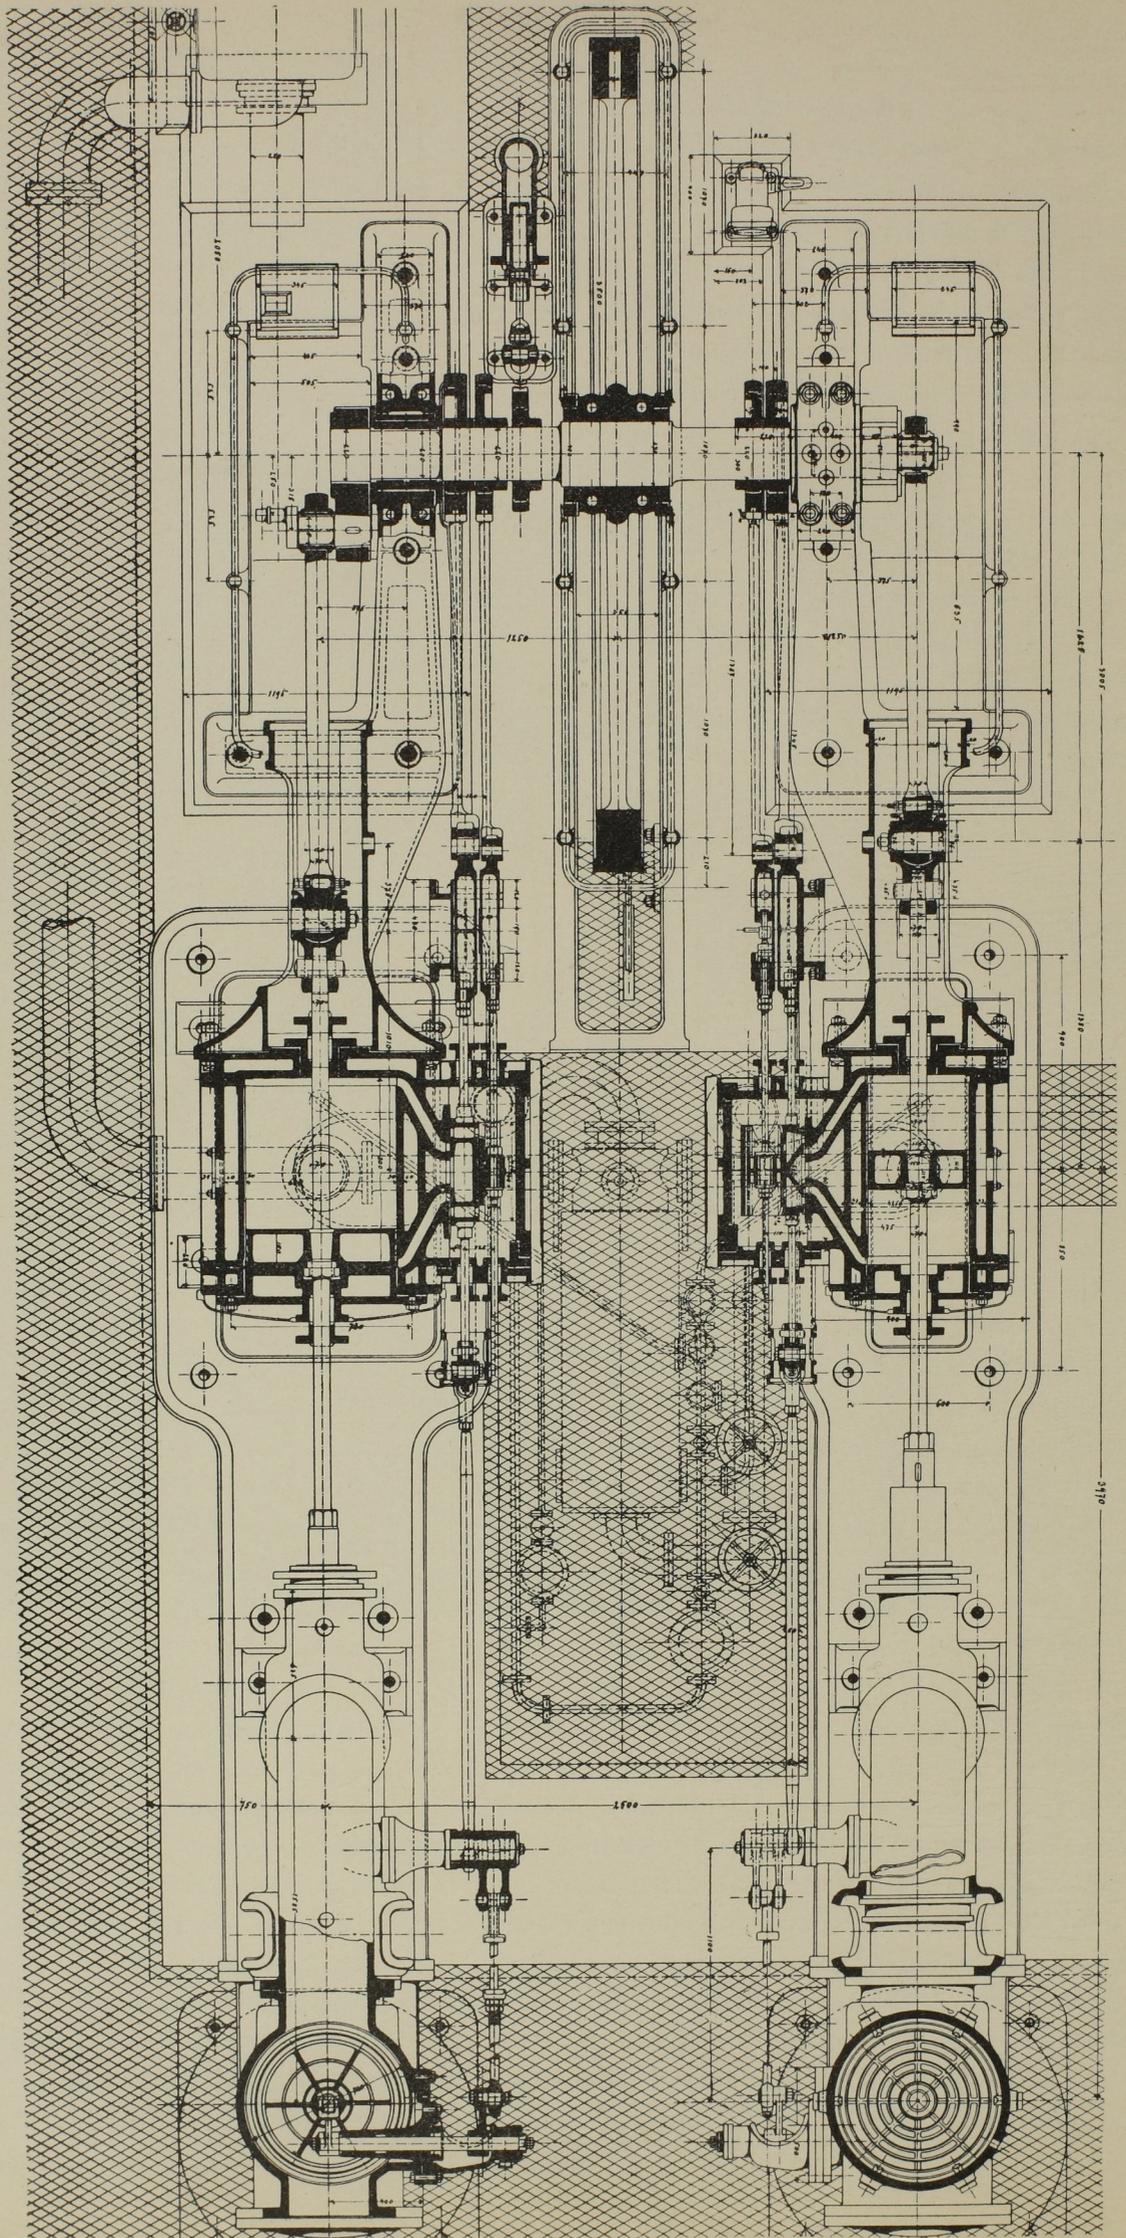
Grundriss und Längsschnitt der Pumpmaschine. Massst. 1:30.
